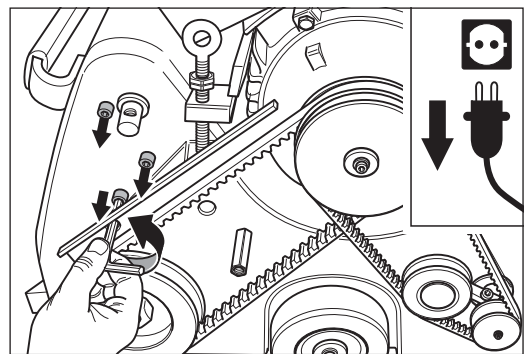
Mit einer Hand das Aggregat festhalten und gleichzeitig die drei Befestigungsschrauben des Aggregats entfernen.
